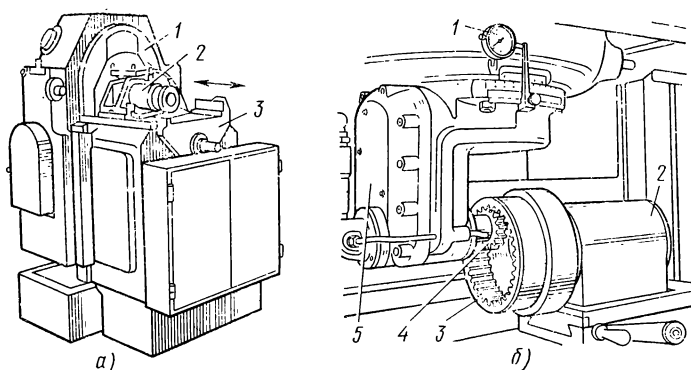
Оборудование для шевингования зубчатых колес внутреннего зацепления:
